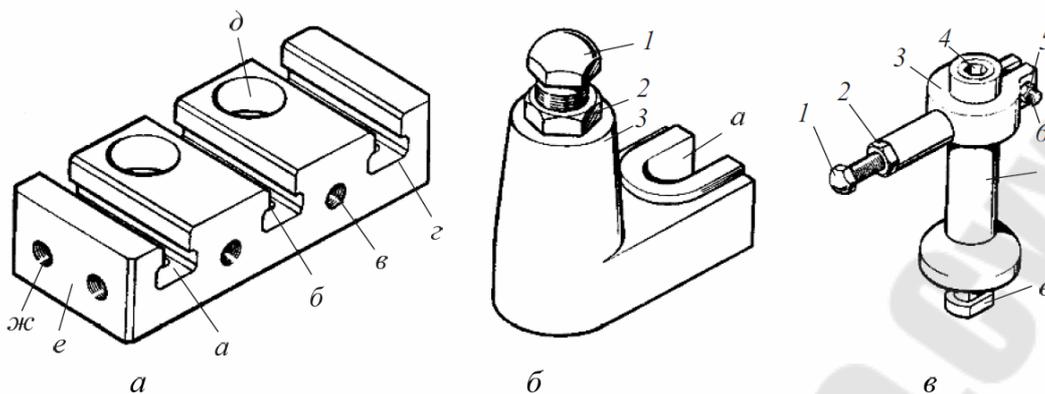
Установочные детали и сборочные единицы сборно-разборного приспособления [4]
